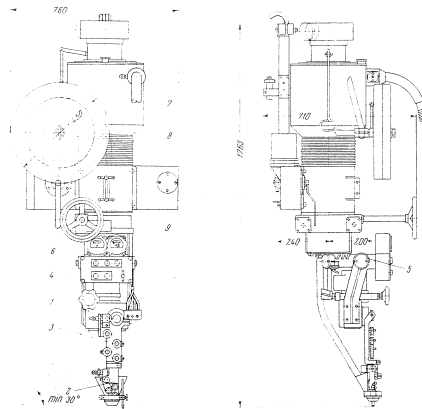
Чертеж общего вида сварочного автомата АВС с габаритными размерами и обозначениями основных узлов, расшифрованных в тексте
